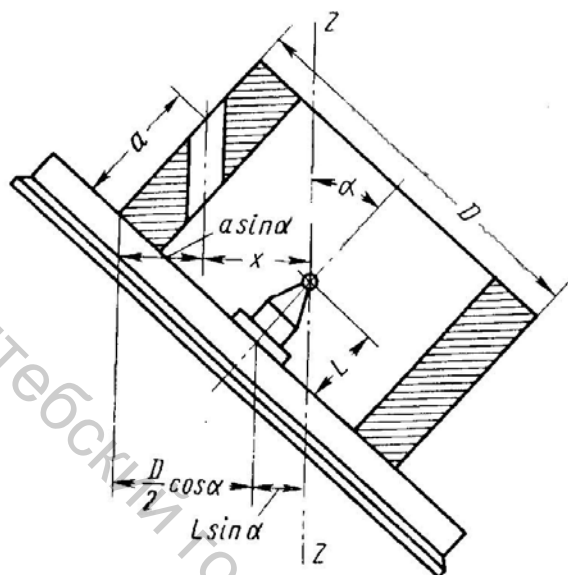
Схема настройки для обработки под углом α на расстоянии a
